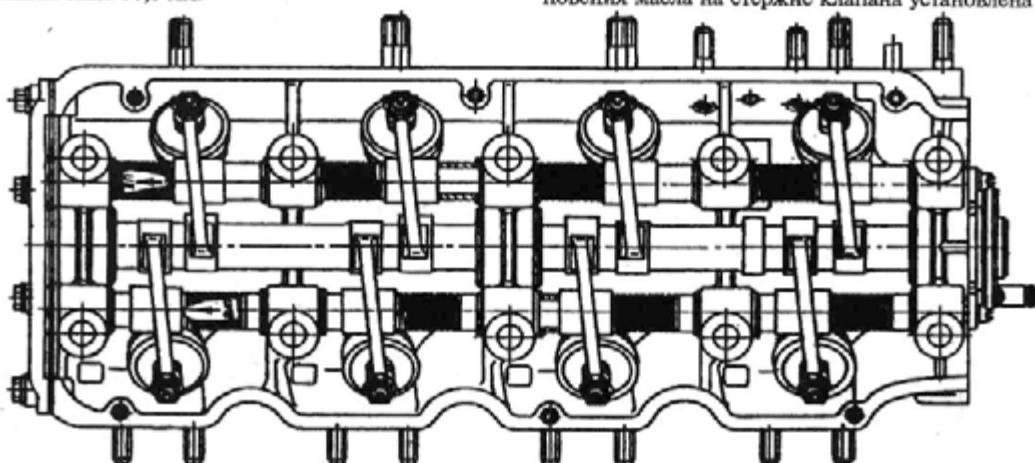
Расположение на головке цилиндров деталей привода клапанов
